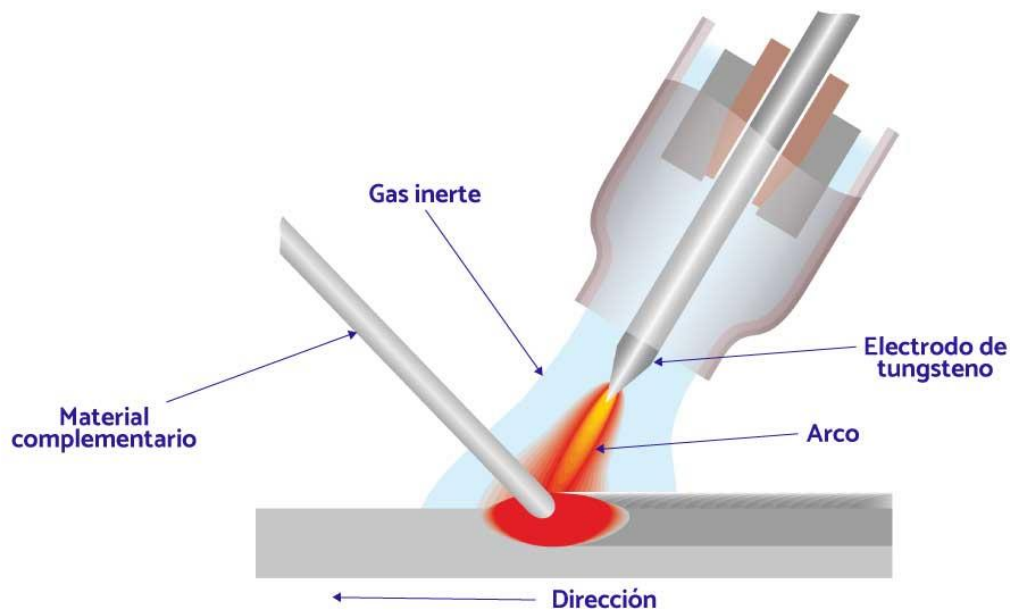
Dibujo esquemático del proceso de soldadura TIG (Fuente: www.metaltechgroup.es).
